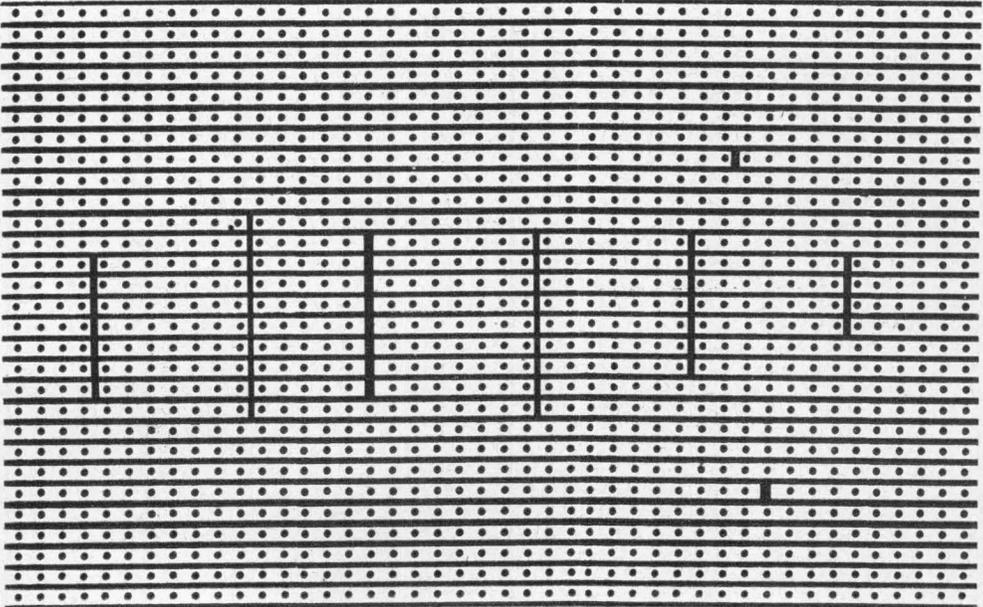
Plaqueta de circuito impresso universal utilizada nesta montagem, vista pelo lado cobreado.
